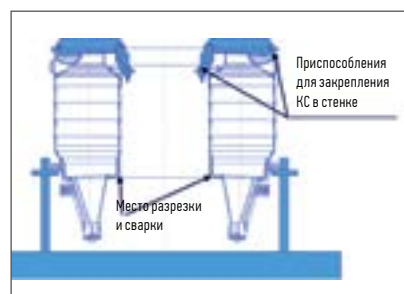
Схема разрезки и последующей сварки КС
